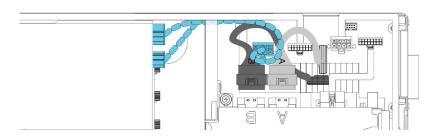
Reconectando o cabo do conjunto da placa riser frontal auxiliar com o nó de expansão
